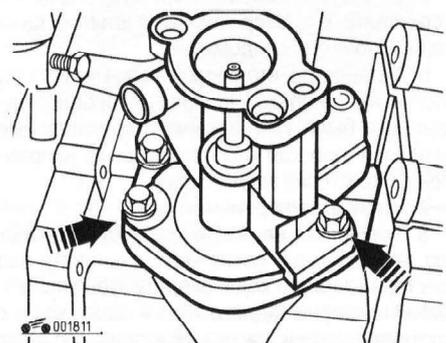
Расположение болтов крепления вала механизма переключения передач
